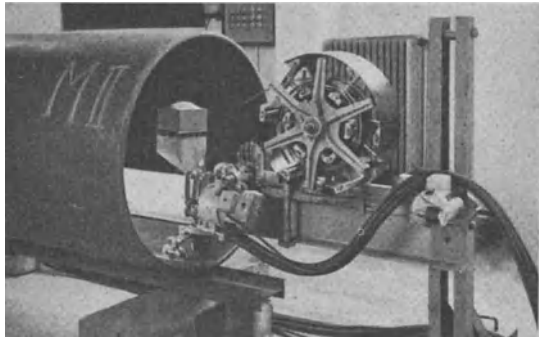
Ellira-Schweißeinrichtung für das Schweißen im Innern von Behältern.
